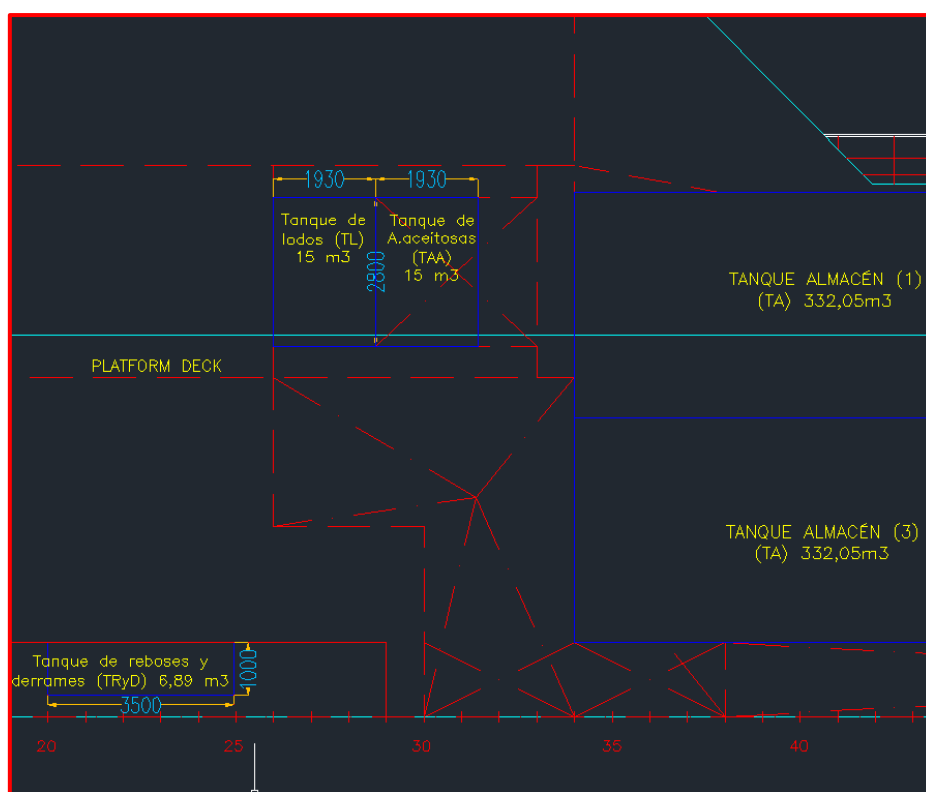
Tanque de lodos / vista estribor (alzado)
